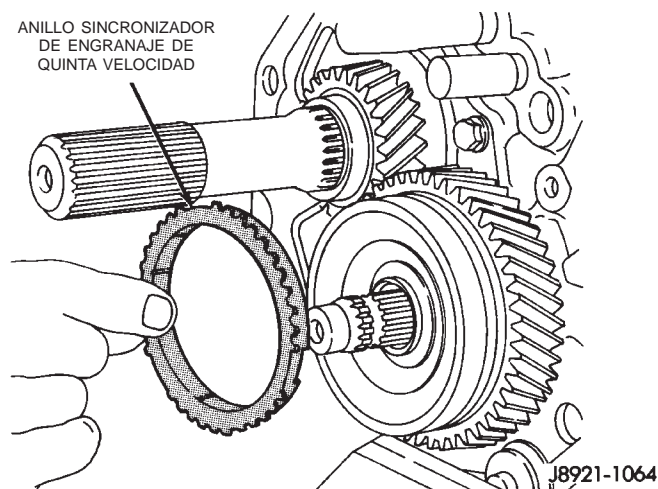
Desmontaje de anillo sincronizador de engranaje de quinta velocidad
